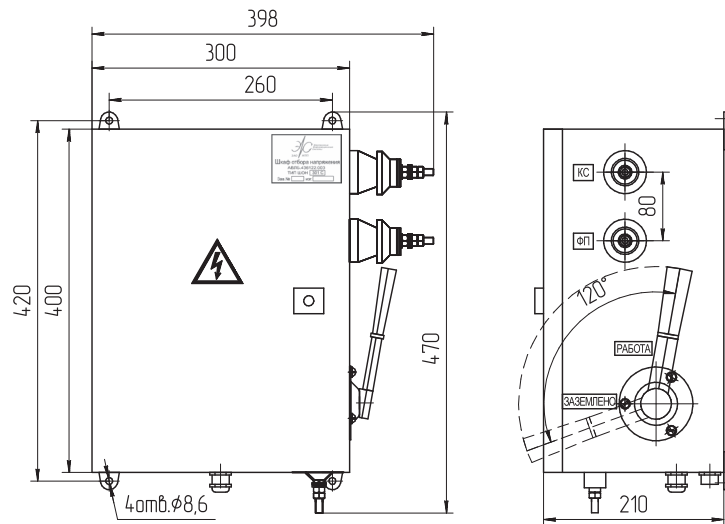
Габаритно-присоединительный чертеж ШОН-301С.
